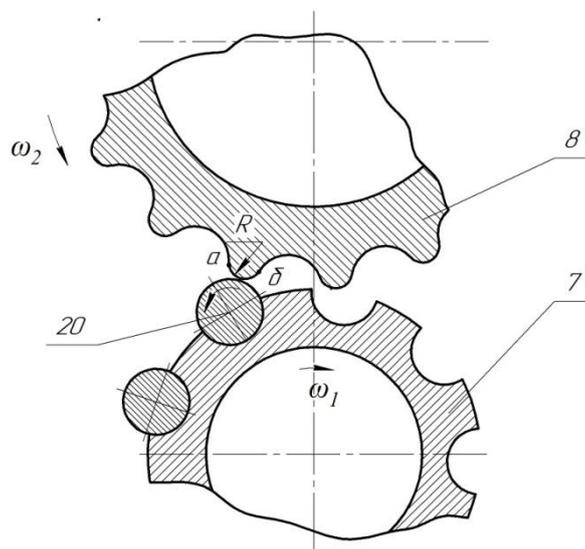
Схема профилей зубьев ведущих и ведомых колес
